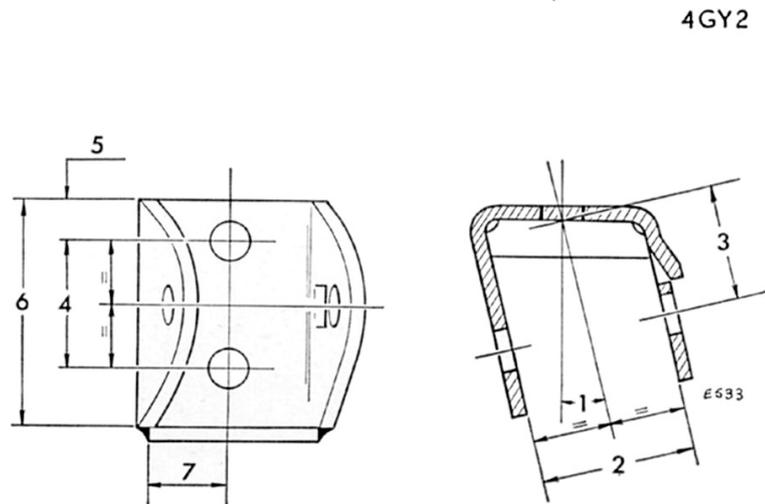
Jambe de force arrière (Herald 1200, 12/50, 13/60 et Vitesse)
